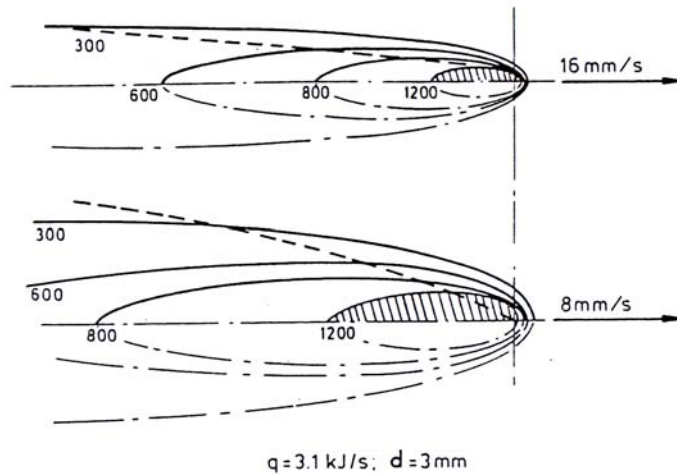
Efecto de la velocidad de soldadura en la forma de las isotermas en un acero al carbono (74).
